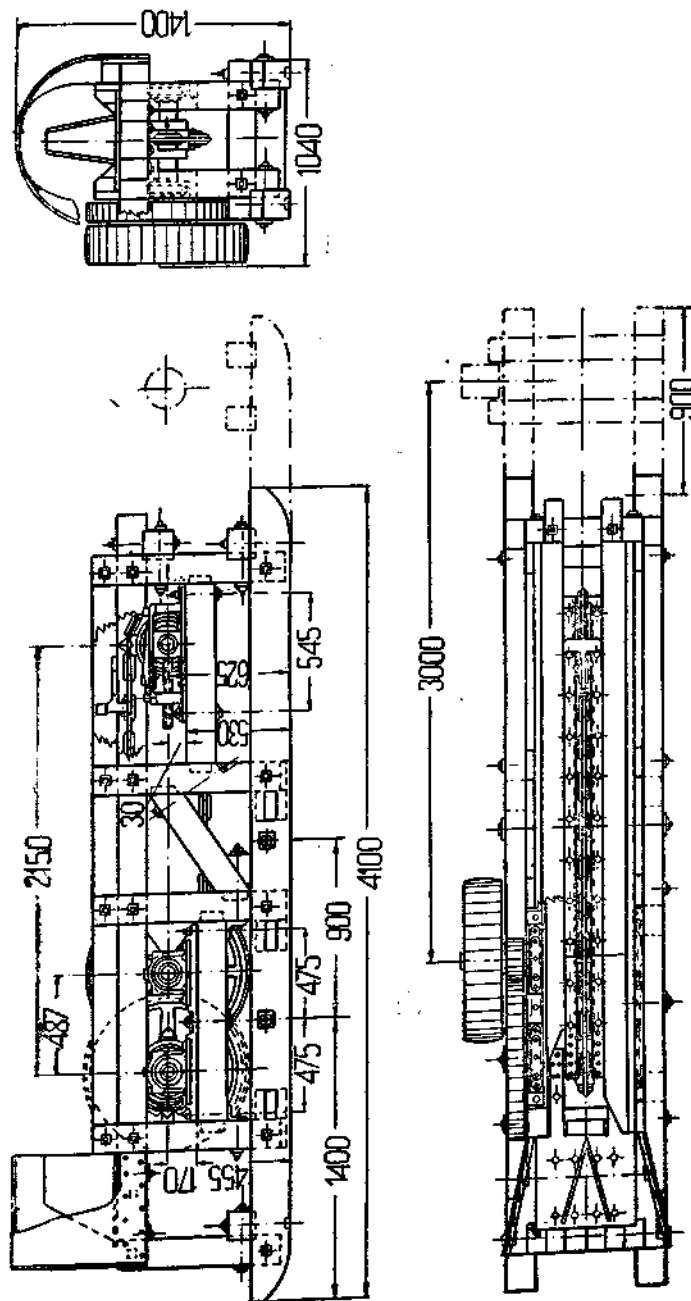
Механический цепной колун типа Севлеса конструкции ЦНИИМЭ
